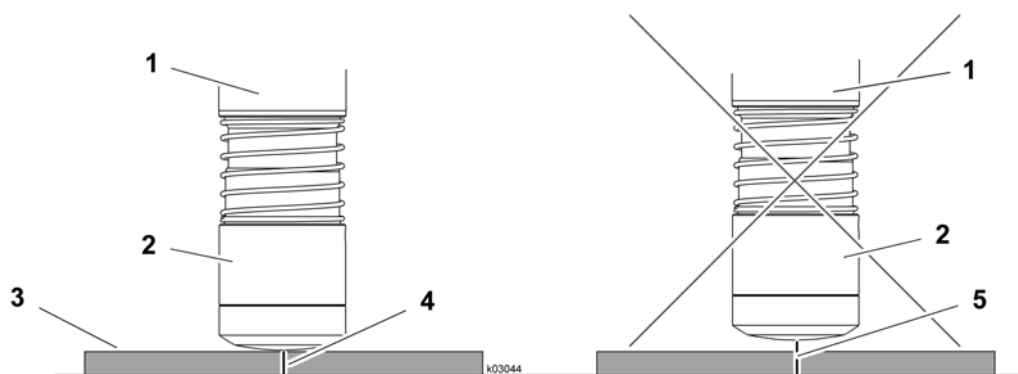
Scelta delle dimensioni della lama (con pattino a molla)
